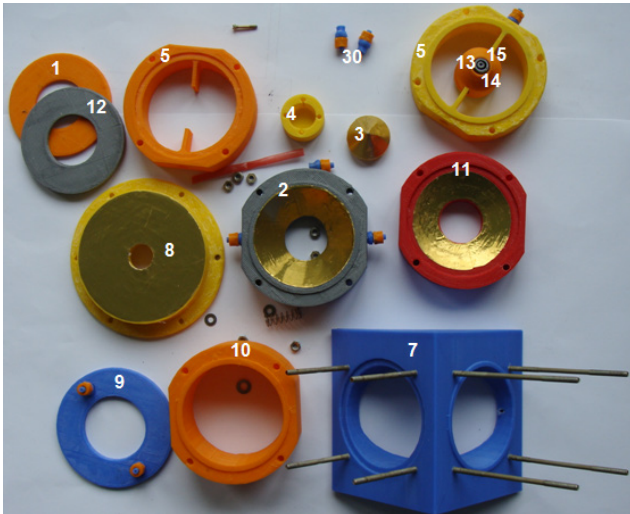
Надруковані деталі оптичної системи для концентрації лазерного проміння на поверхні оброблюваної заготовки
